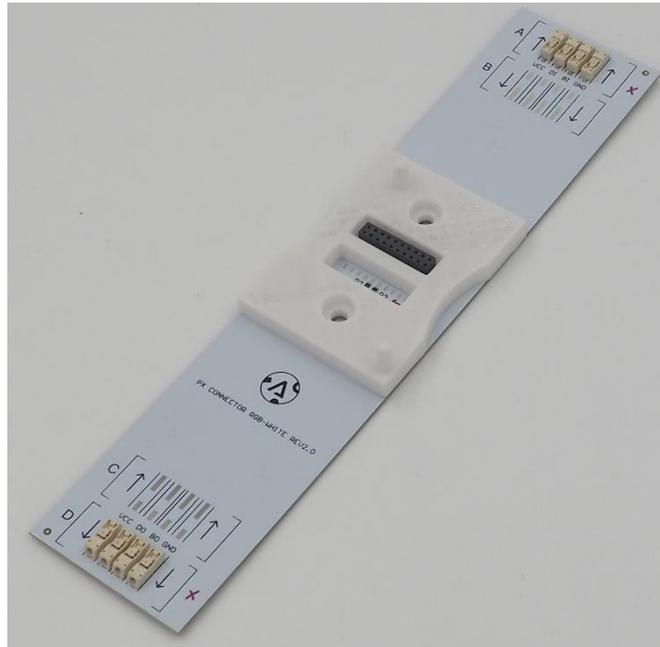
Unión entre PCB de conexión vertical y soporte 3D.
